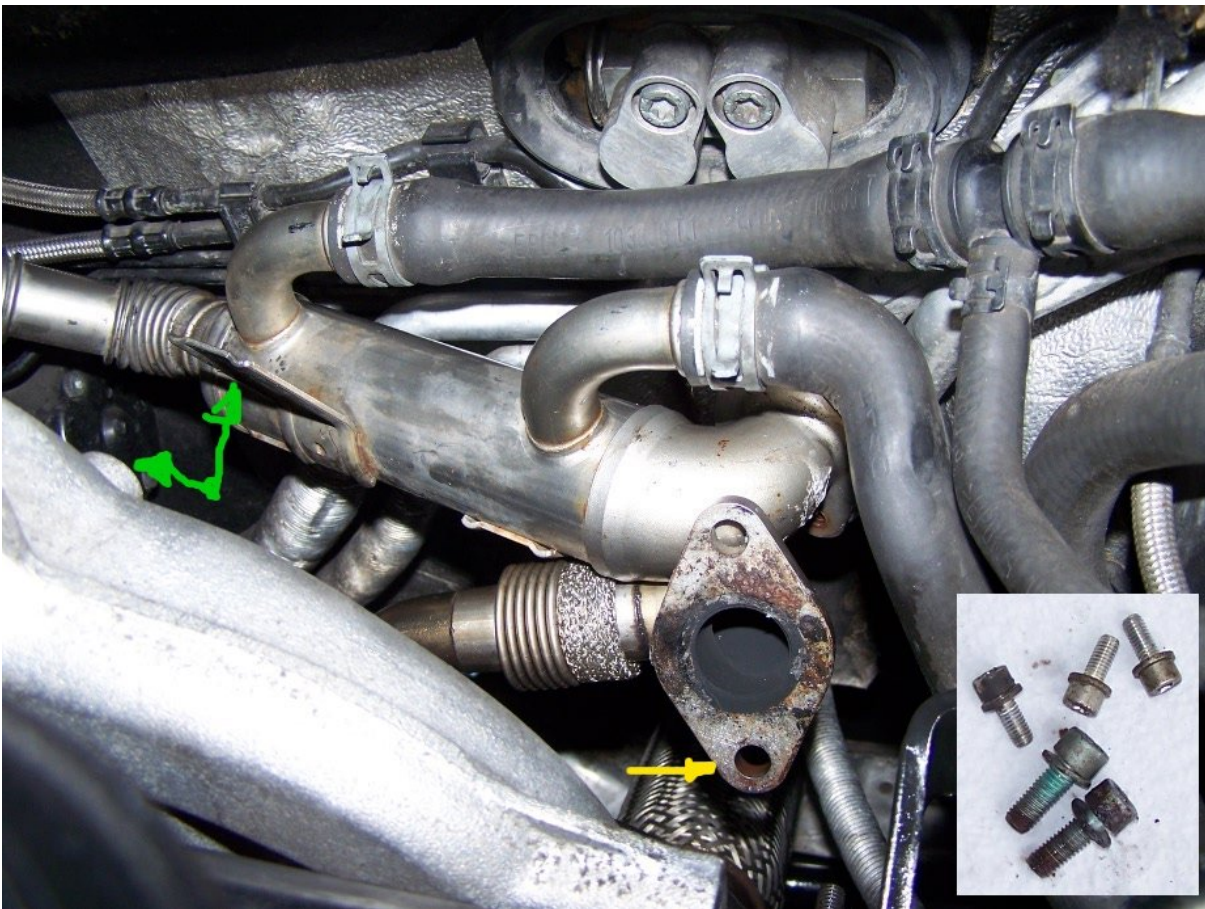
Gelöster und weggeschwenkter Abgaskühler und Schrauben
